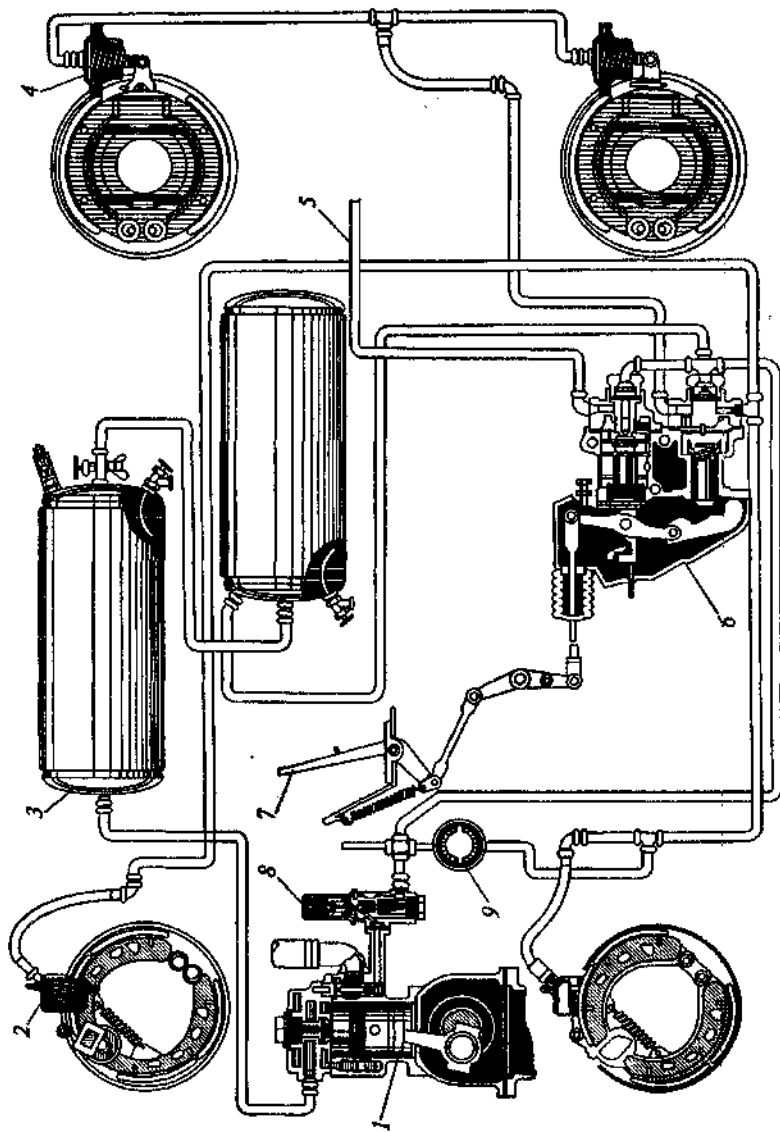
Пневматический тормозной привод: 1 — компрессор; 2 и 4 — тормозные камеры; 3 — баллон; 5 — трубопровод; 6 — кран; 7 — педаль; 8 — регулятор; 9 — манометр
